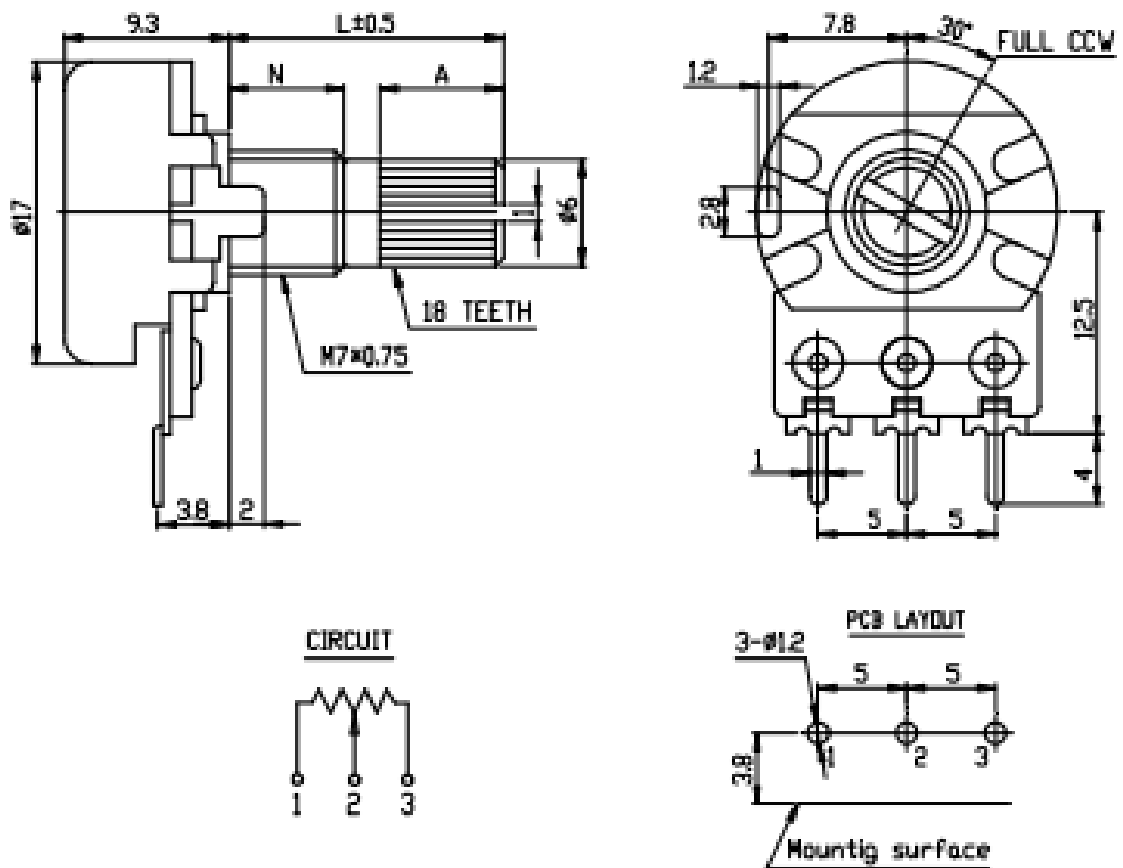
Габаритні розміри резистора 16T1-B100K
